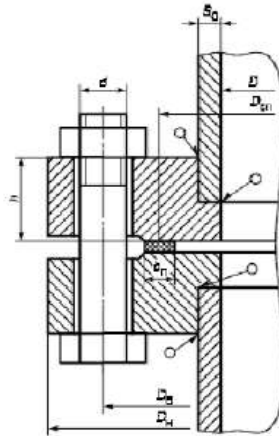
Фланцевое соединение с гладкой уплотнительной поверхностью
